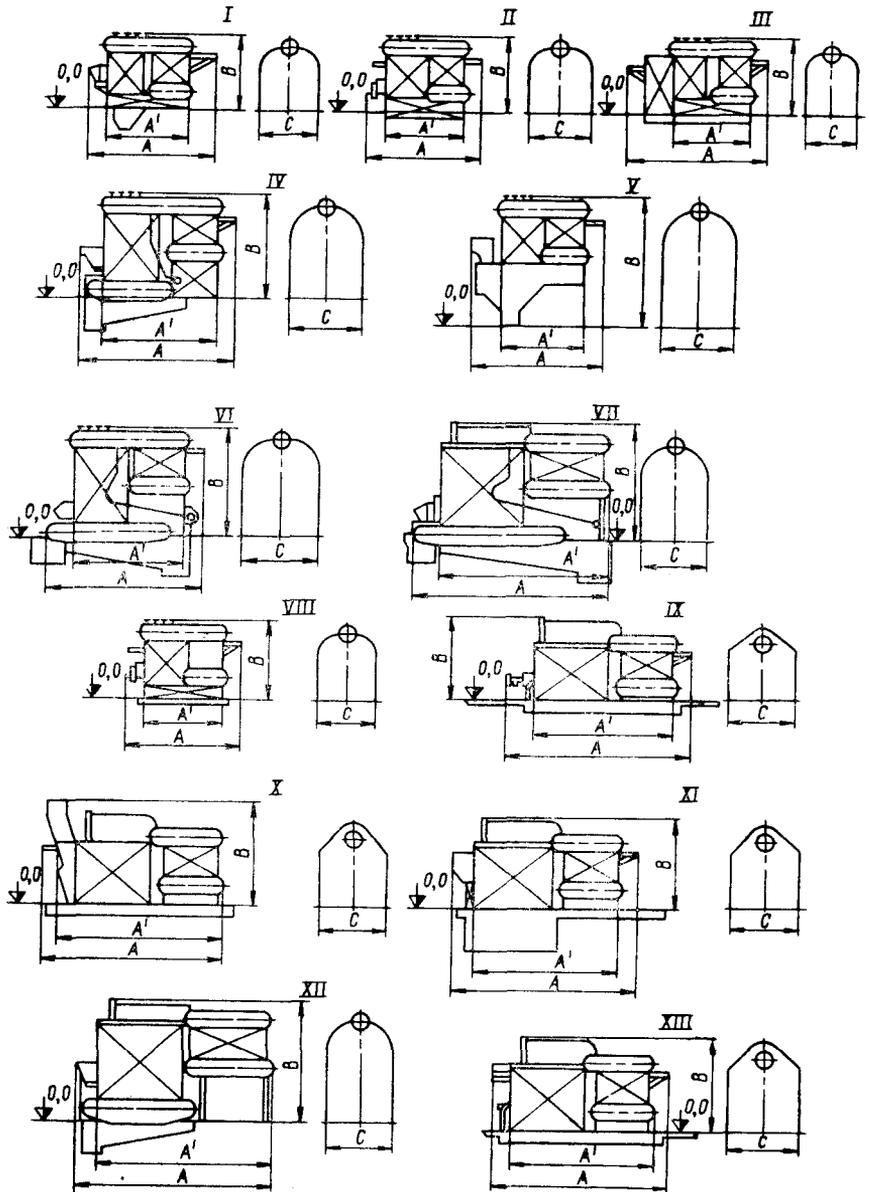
Схемы и габаритные размеры компоновок котлов типа ДКВР с различными топочными устройствами:
